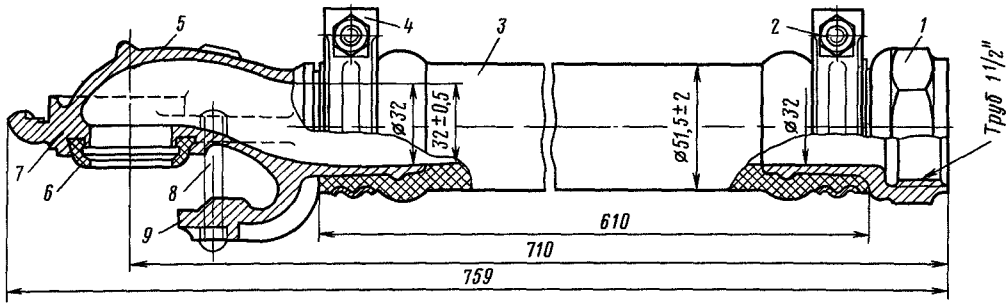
Соединительный разъемный рукав типа P1 (ГОСТ 2593—69)
